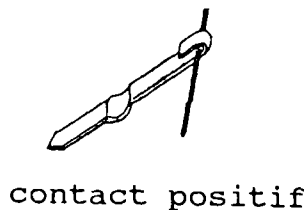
Dans une feuille métallique, découper deux morceaux de dimensions 5mmx40mm environ, pour réaliser les contacts. Découper une extrémité de chaque pour former une pointe et replier sur elle-même l'extrémité opposée. Donner à la pièce formant le contact positif la forme montrée sur le schéma.
